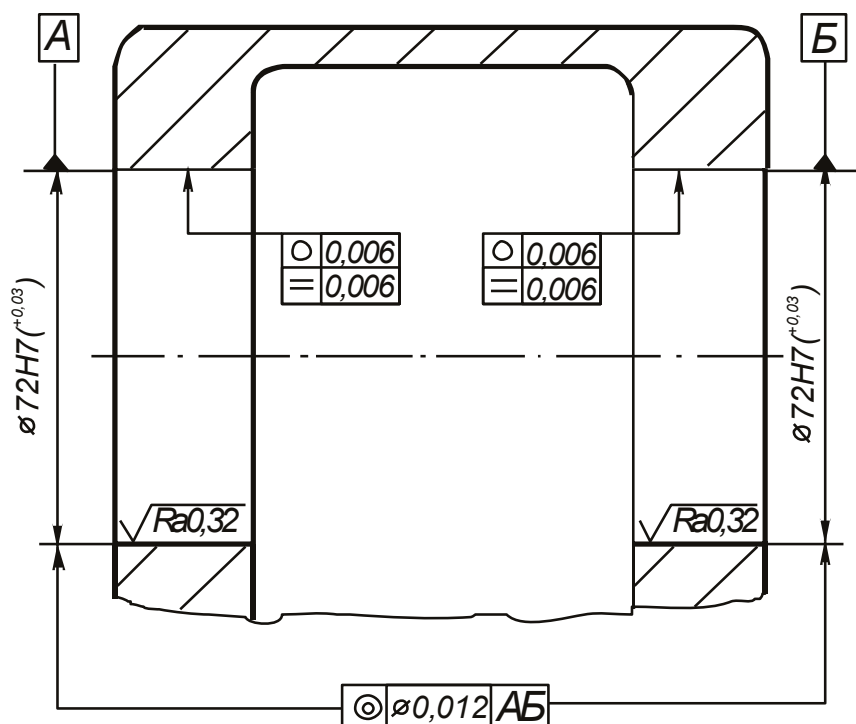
Пример обозначения требований к точности поверхностей отверстий корпуса, сопрягаемых с наружными кольцами подшипников качения
